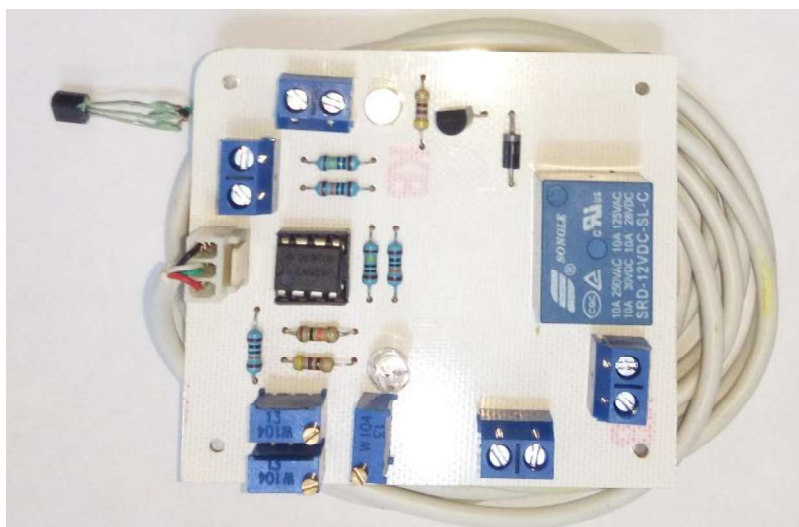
Tarjeta KIT INST-02 ensamblada.
